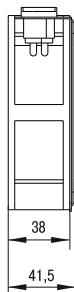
Габаритные и установочные размеры ПВ / Figure 1 – Overall and installation dimensions of the FP / 1 – suret – DP gabarittik jäne ornatu ölçemderi / Рисунок 1 – Габаритні та установочні розміри ПВ
